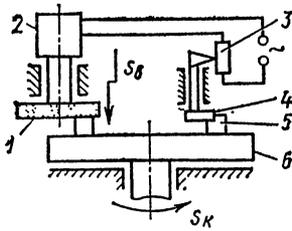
Схема автоматической подналадки плоскошлифовального станка для уменьшения влияния износа на точность обработки
